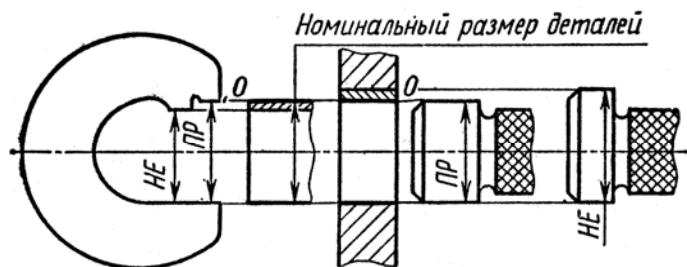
Схема для выбора номинальных размеров предельных гладких калибров
